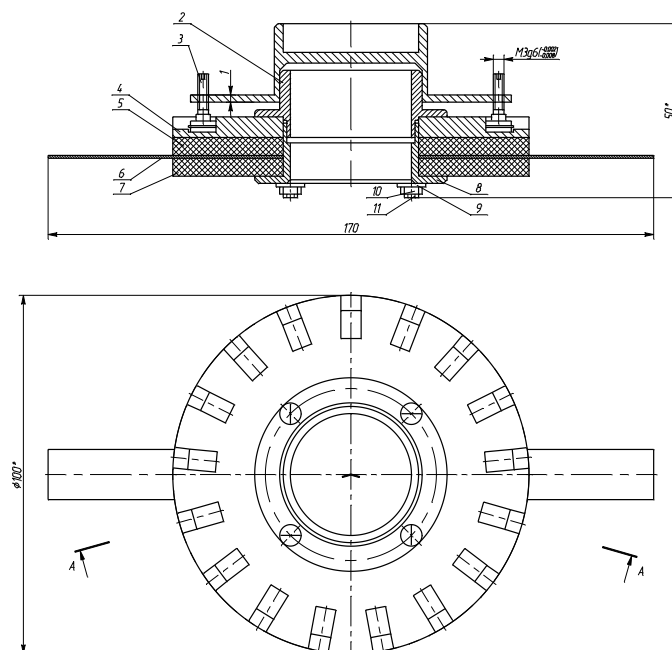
Приспособление для сварки чувствительных элементов
